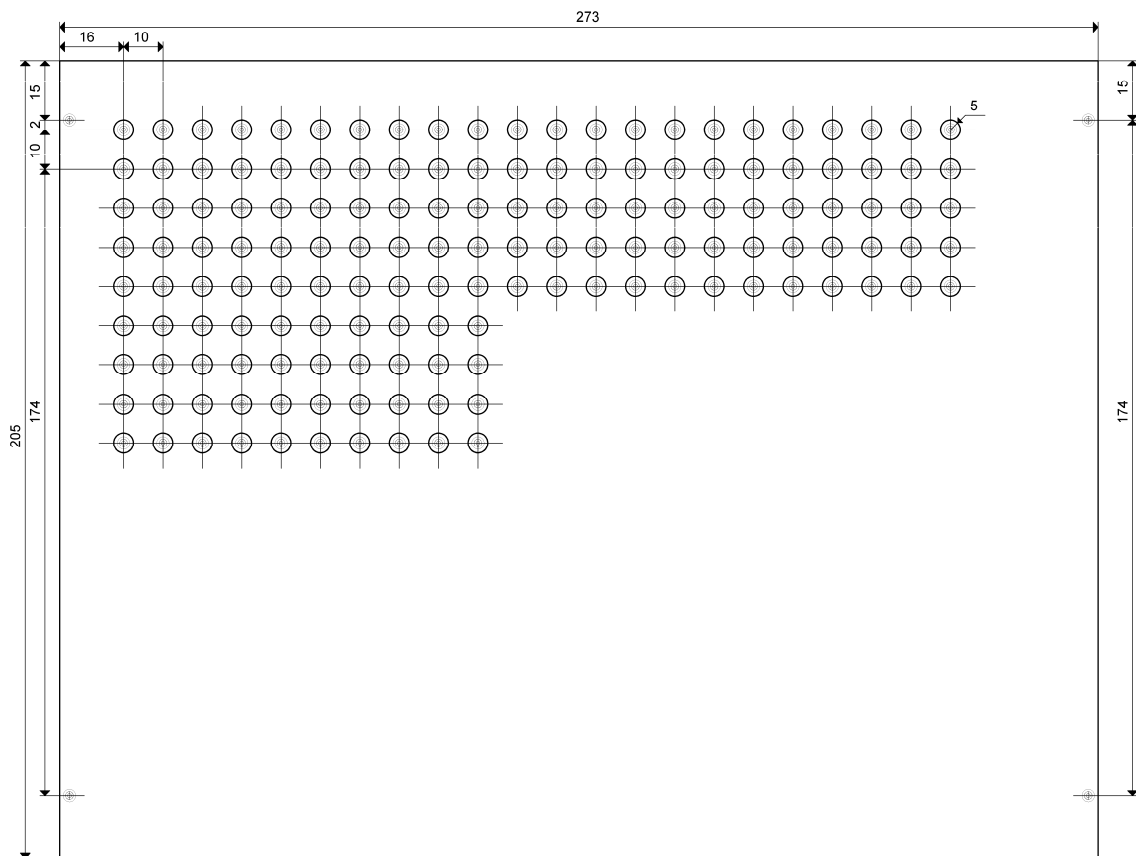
Konstrukční náčrt zadního panelu zařízení
